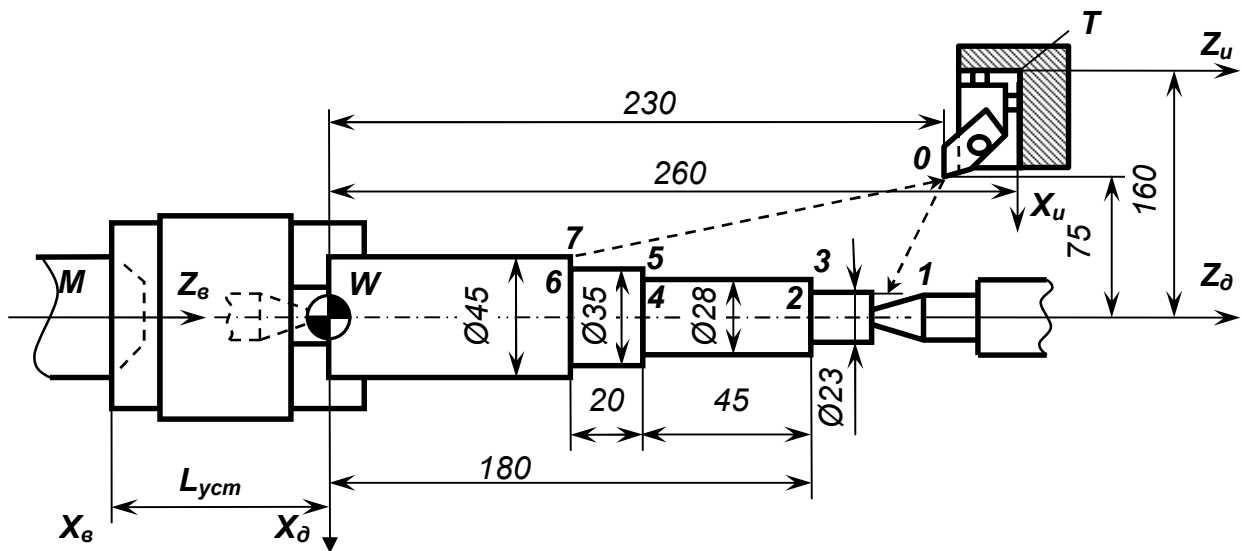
Операційний ескіз обробки вала на токарному верстаті з ЧПК
